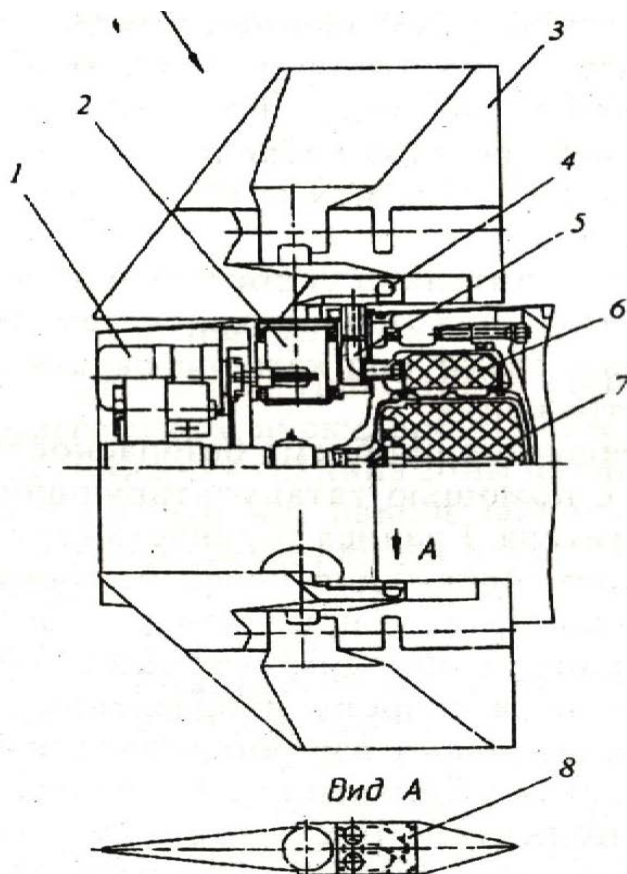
Газодинамическое устройство склонения ракеты: 1 – рулевой привод на горячем газе; 2 – ось руля; 3 – консоль руля; 4 – газоструйное сопло; 5 – внутренний газовод; 6 – газогенератор системы склонения; 7 – газогенератор рулевых приводов; 8 – выходной газовод
